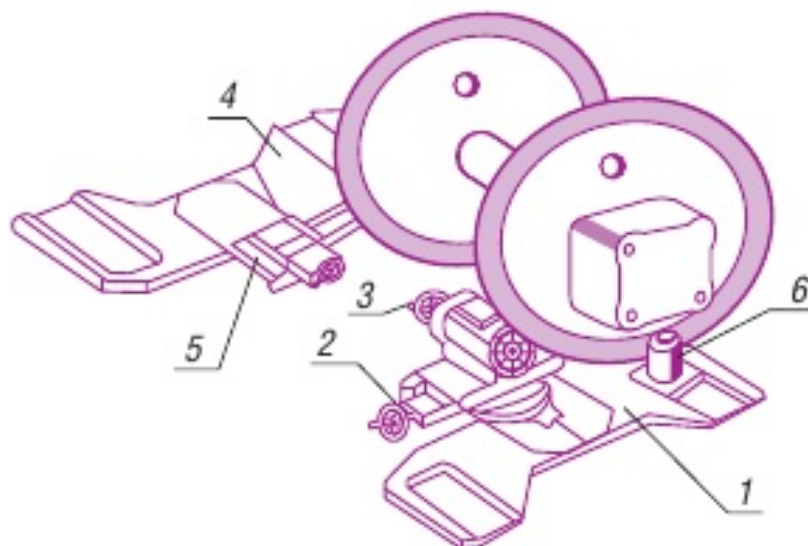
Общий вид мобильного станка с колёсной парой [31]:
